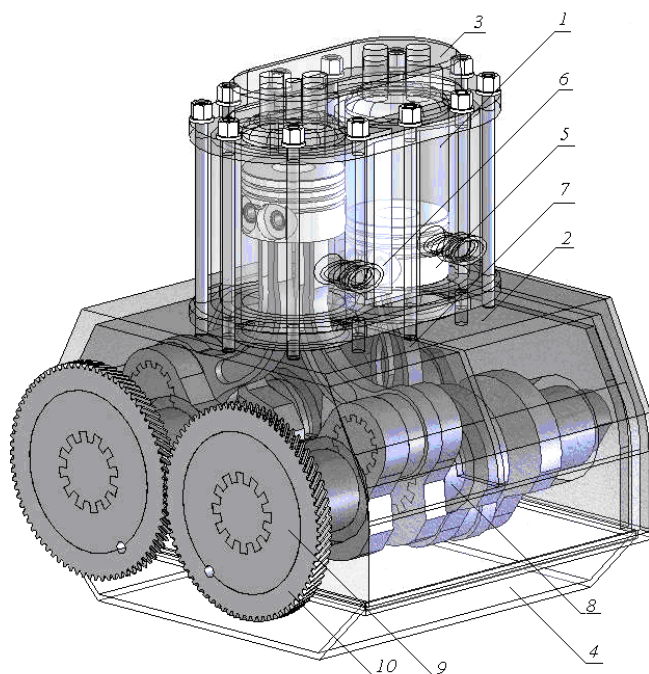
Общий вид ДВС с кривошипно-шатунным механизмом со сдвоенными кинематическими связями с шатунами серповидной формы:
